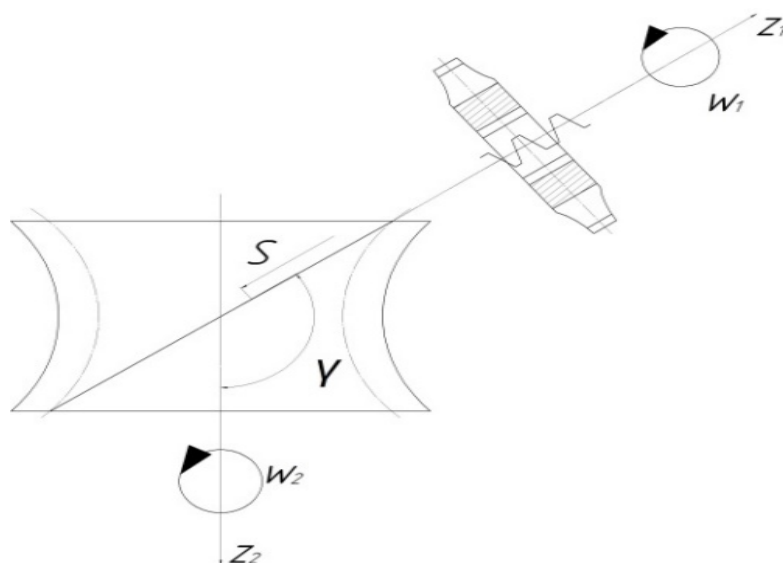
Схема формообразования винтовой зубчатой поверхности.
